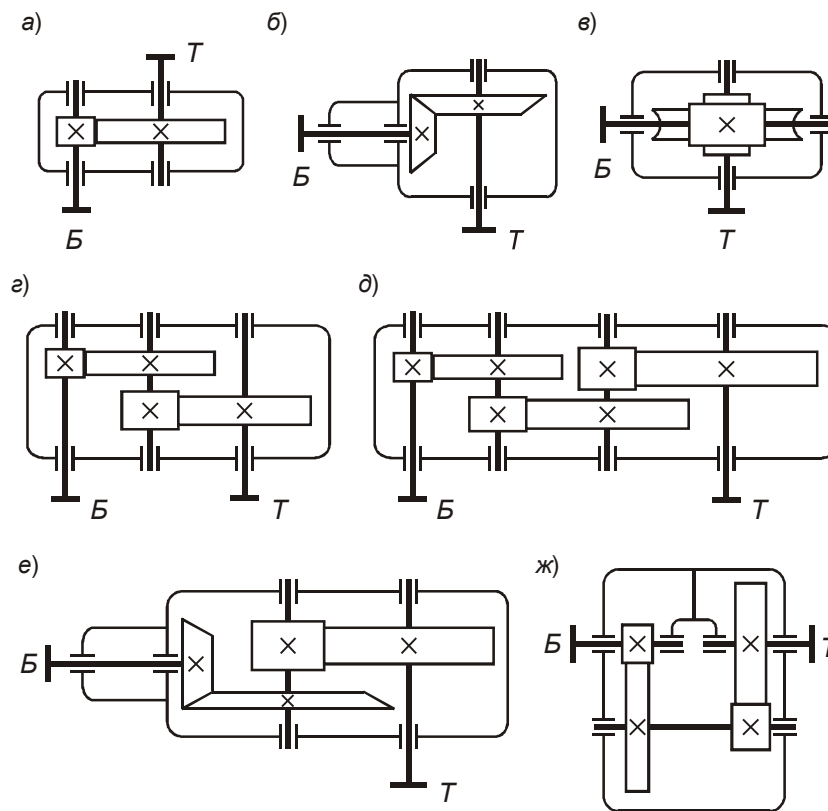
Схемы редукторов: а – цилиндрический одноступенчатый; б – конический одноступенчатый; в – червячный одноступенчатый; г – цилиндрический двухступенчатый развернутой схемы; д – цилиндрический трехступенчатый развернутой схемы; е – коническо-цилиндрический двухступенчатый; ж – соосный двухступенчатый
